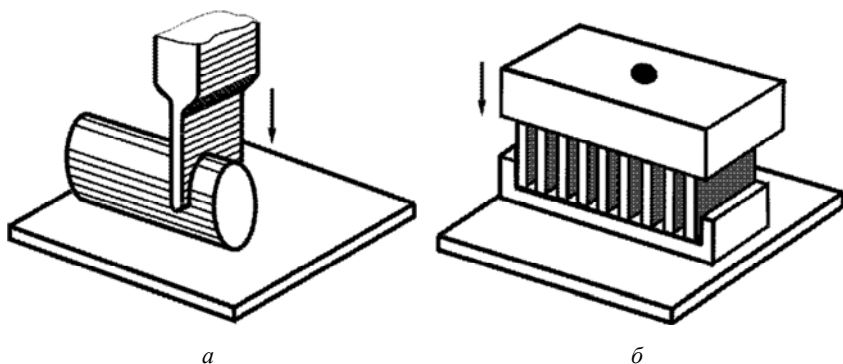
Схема ультразвукового разрезания заготовок:
